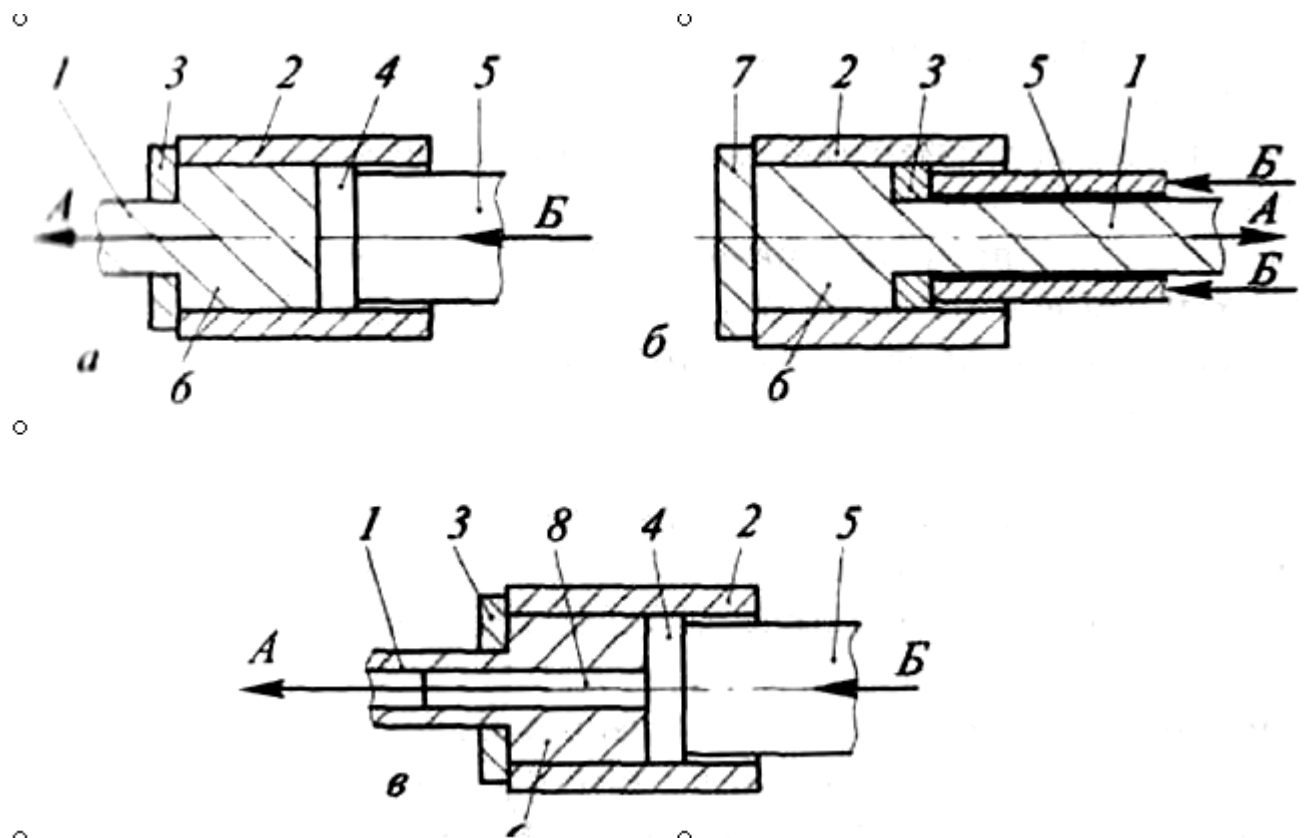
Прямий (а, в) і зворотний методи пресування: 1- виріб; 2 - контейнер; 3 - матриця; 4 - прес-шайба; 5 — пуансон; 6 — заготовка; 7 — кришка; 8 — голка
